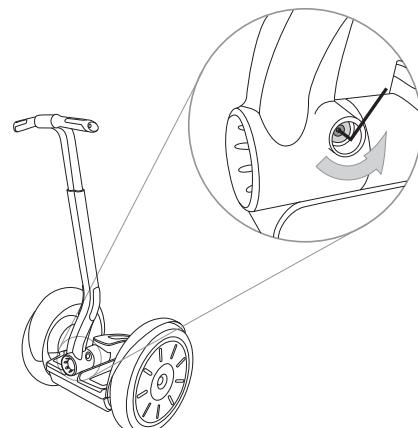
Die LeanSteer-Rahmenschraube entfernen
